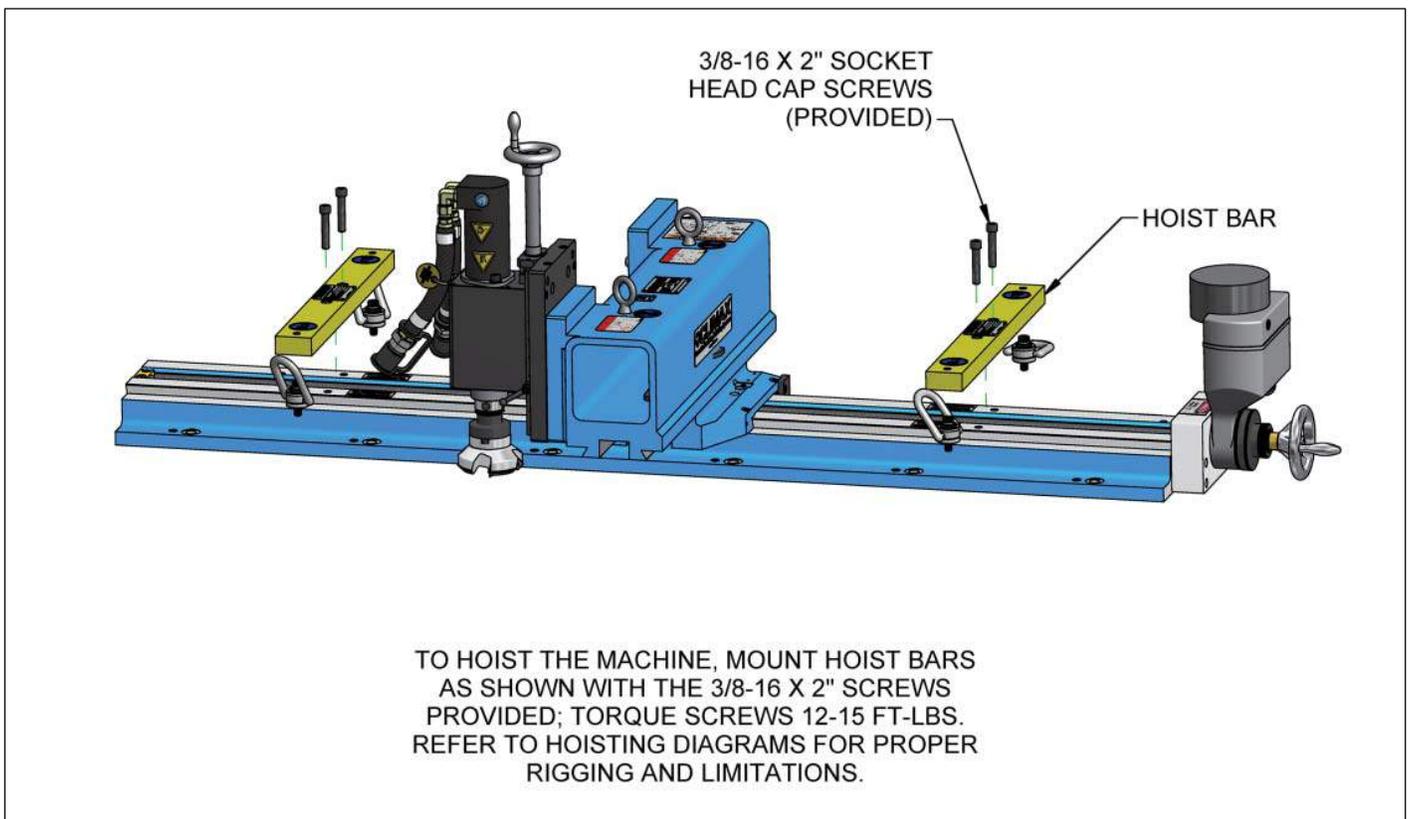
INSTALLATION DE LA BARRE DE LEVAGE
